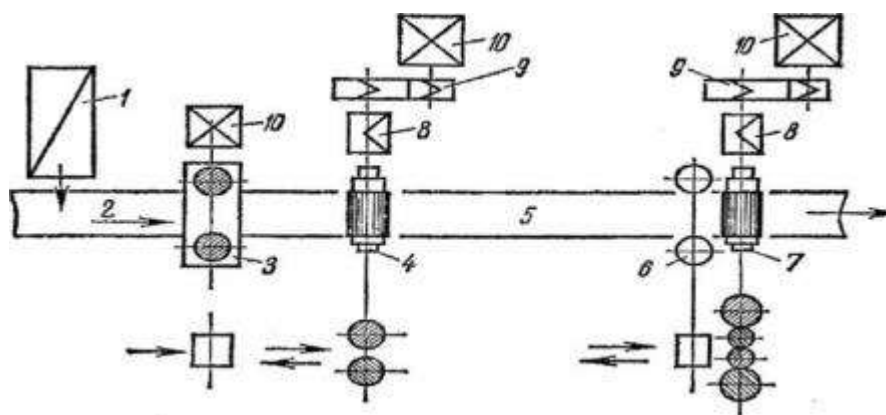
Схема толстолистого стана 2800: 1 – нагревательная печь; 2 – подводящий рольганг; 3 – черновая клеть с вертикальными валками; 4 – черновая двухвалковая реверсивная клеть; 5 – промежуточный рольганг; 6 и 7 – чистовая универсальная четырехвалковая клеть с вертикальными и горизонтальными валками; 8 – шестеренная клеть; 9 – редуктор; 10 – электродвигатель
